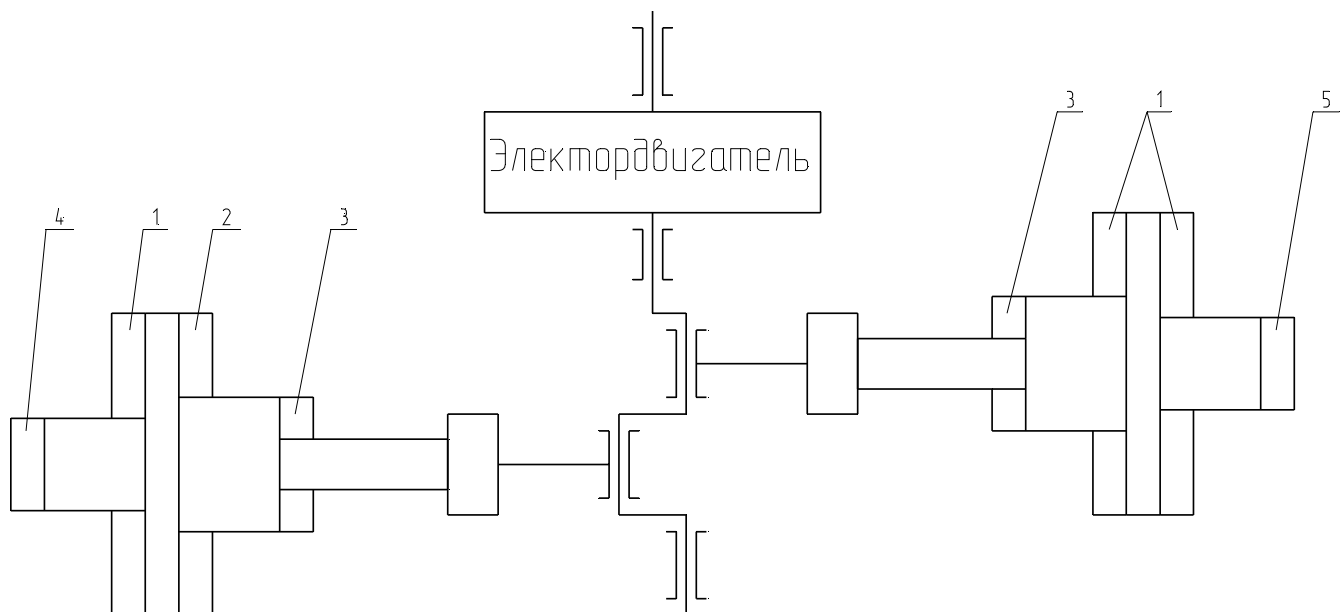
Схема расположения цилиндров в оппозитном пятиступенчатом компрессоре 50Т-130/200
